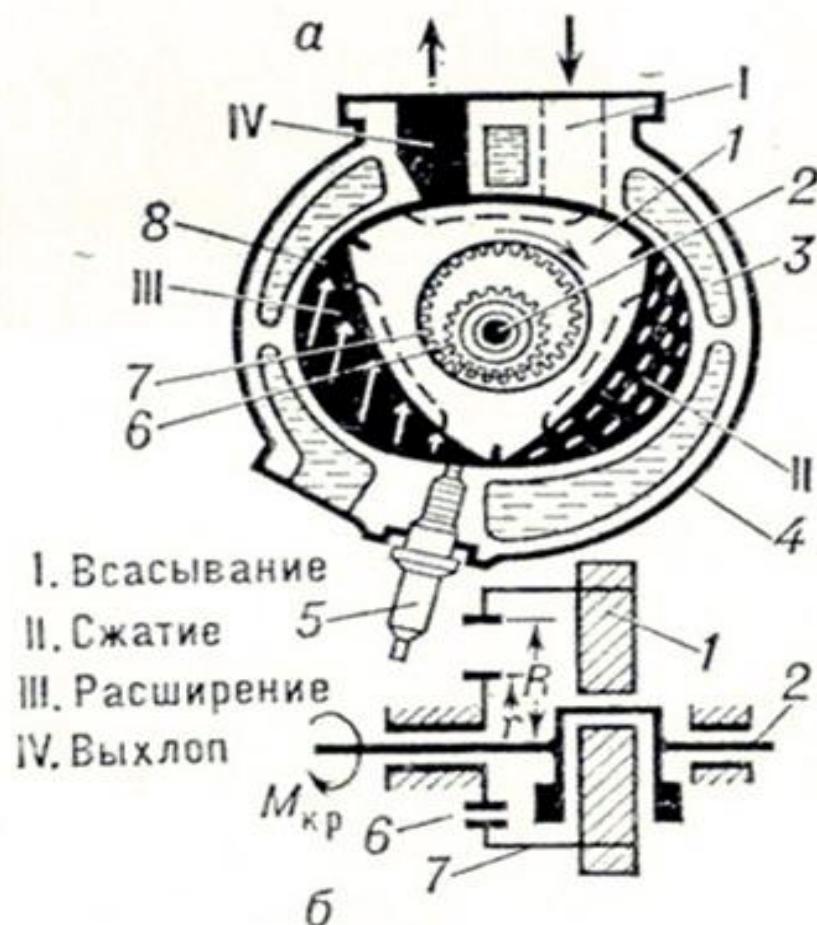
Роторно-поршневой двигатель Ванкеля:
